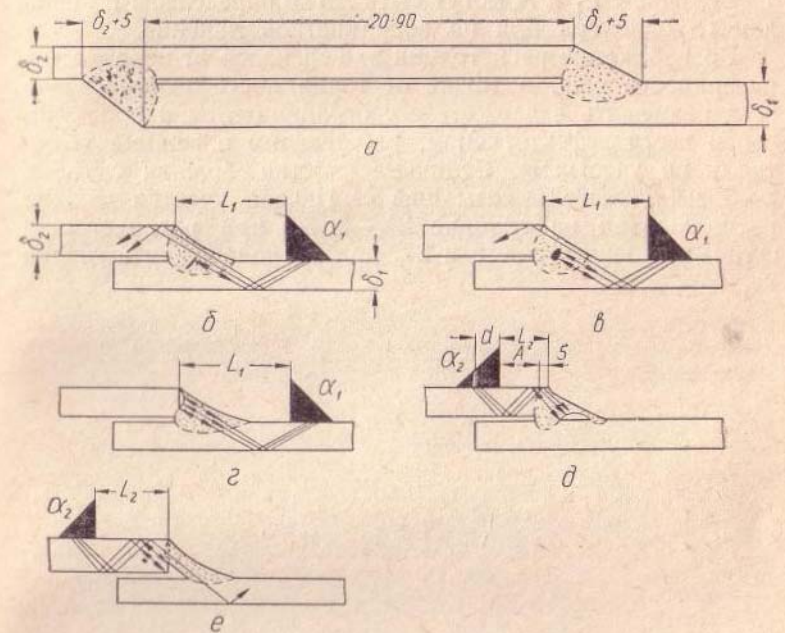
Типовые размеры сварного соединения внахлестку и схемы прозвучивания шва при выявлении дефектов.
